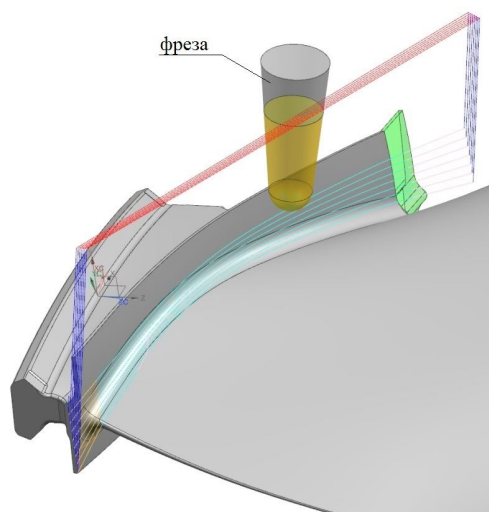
Фрезерование бандажной полки со стороны пера лопатки на станке с ЧПУ ФП-17
